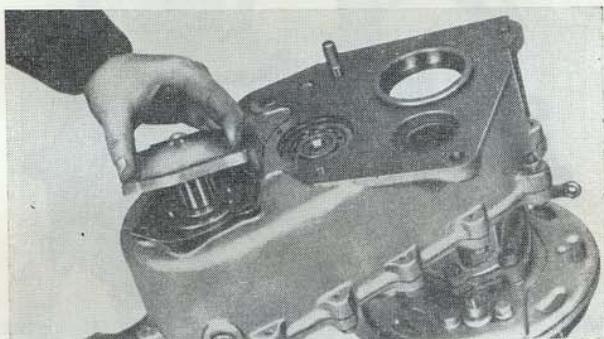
Установка крышки переднего подшипника вала привода переднего моста
